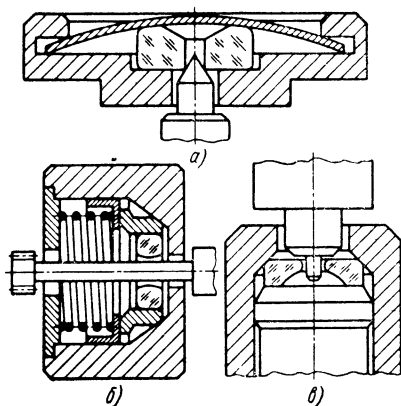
Противоударные устройства конических и цилиндрических открытых опор
